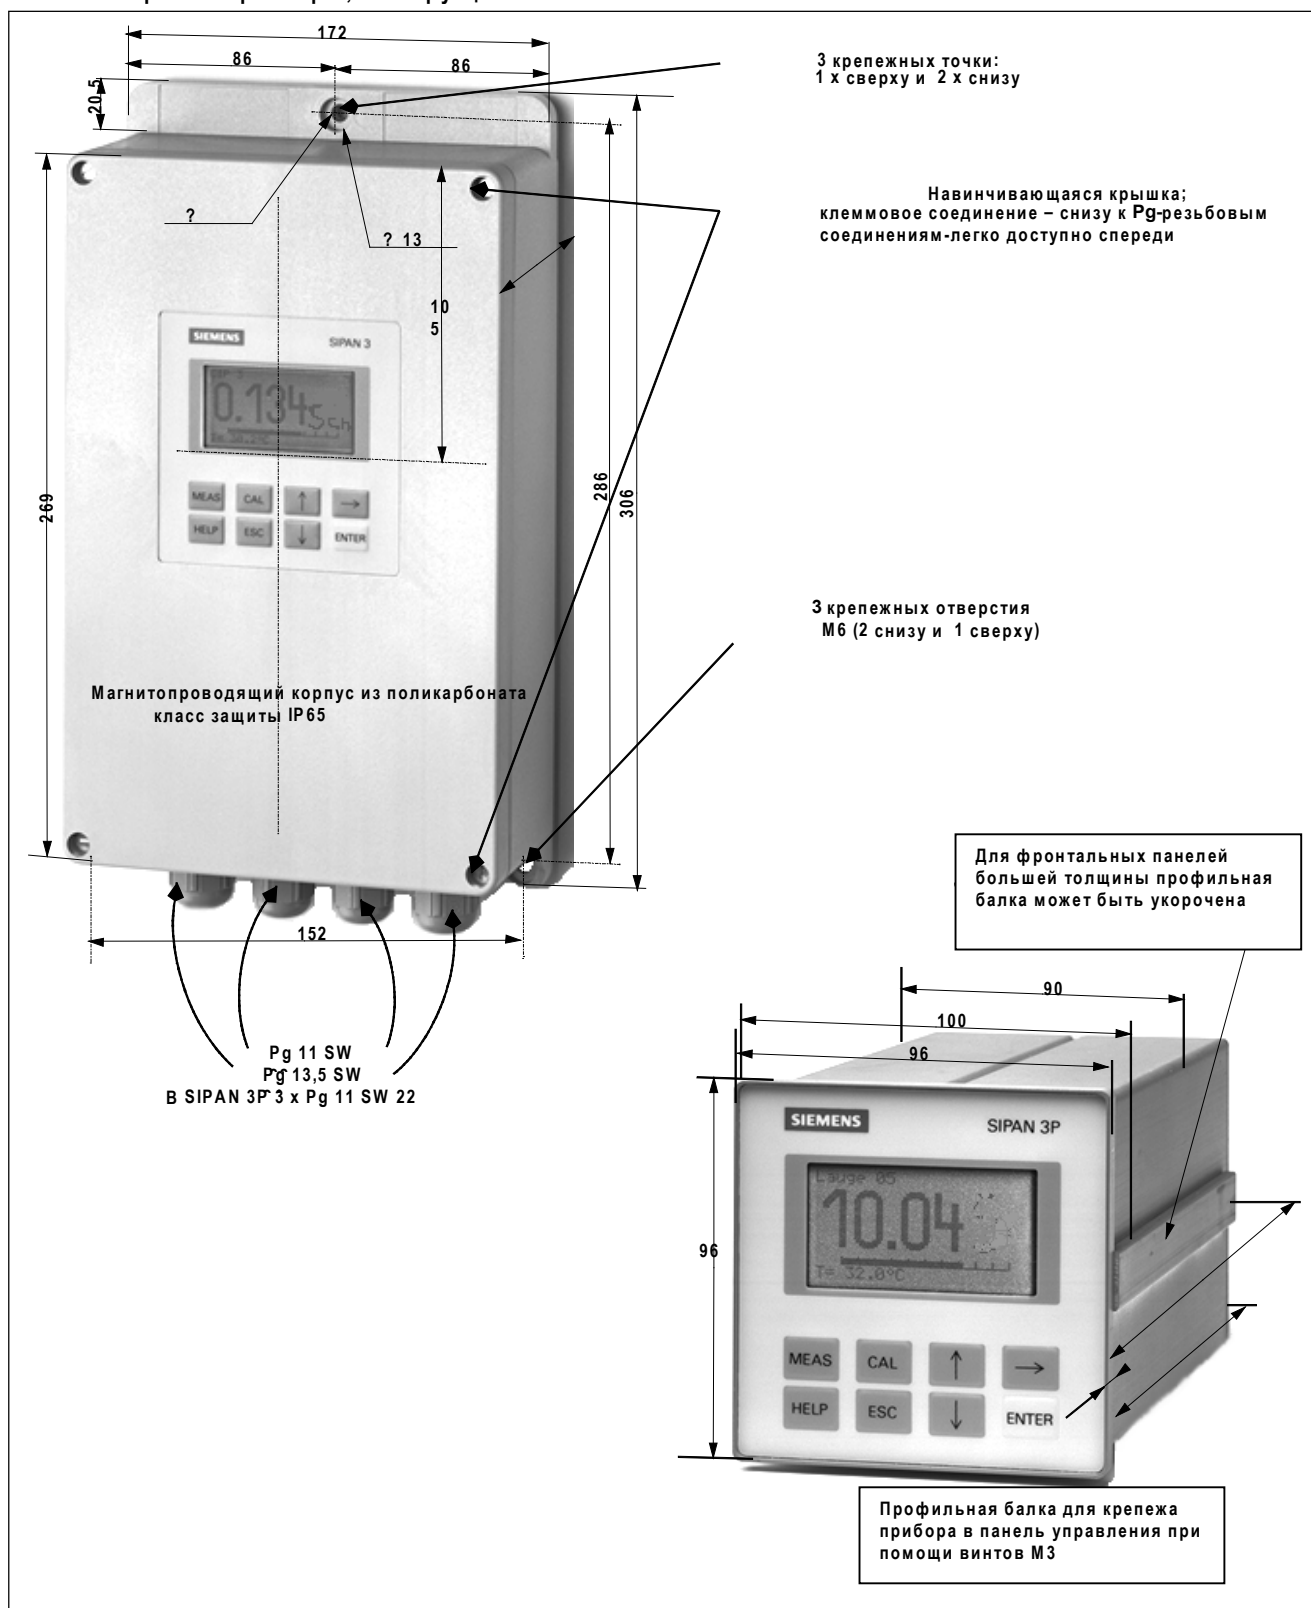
Измерительный преобразователь SIPAN 34, сверху в магнитопроводящем корпусе, снизу в корпусе для установки в панель управления, габаритные размеры
